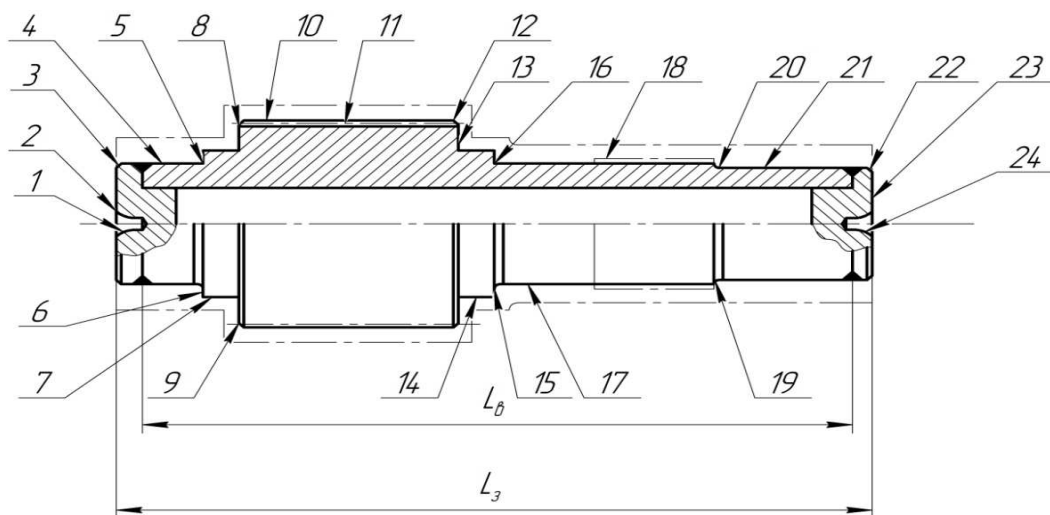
Эскиз сборно-сварной малоотходной пустотелой заготовки вала шлицевого
